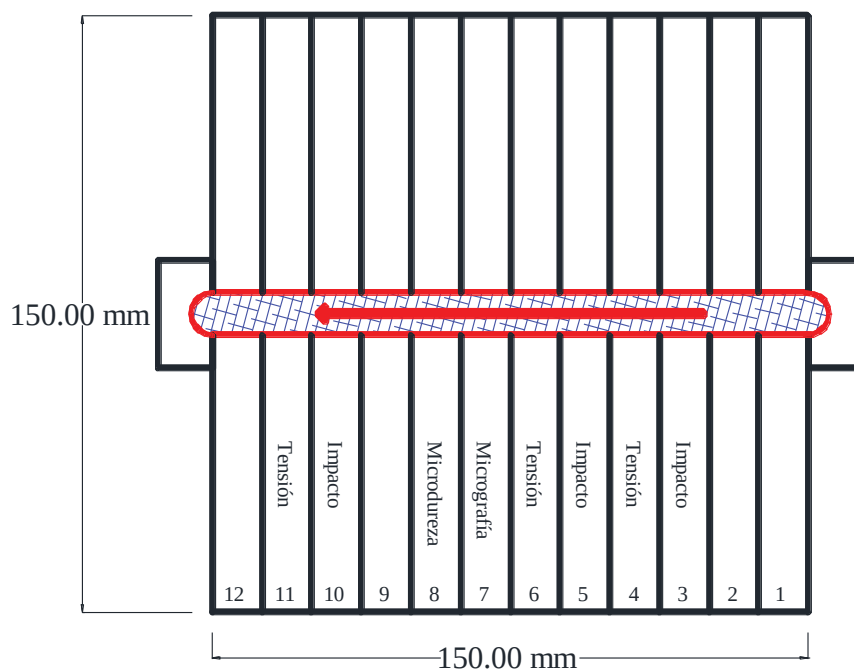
Seccionamiento de la junta soldada.
